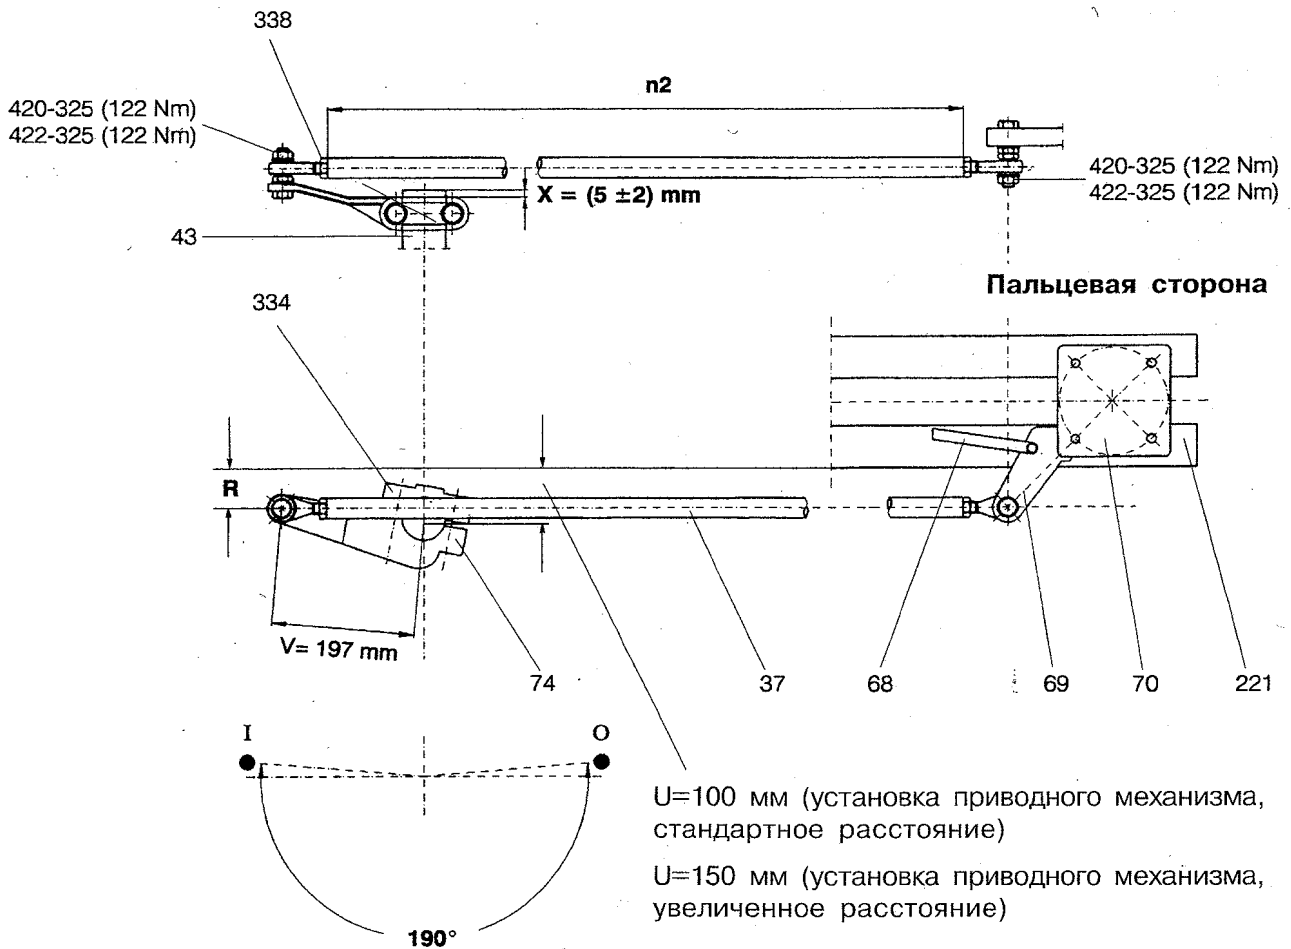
Установка тяг разъединителя: регулировка приводного механизма разъединителя при расположении приводного механизма разъединителя на стороне открывания
